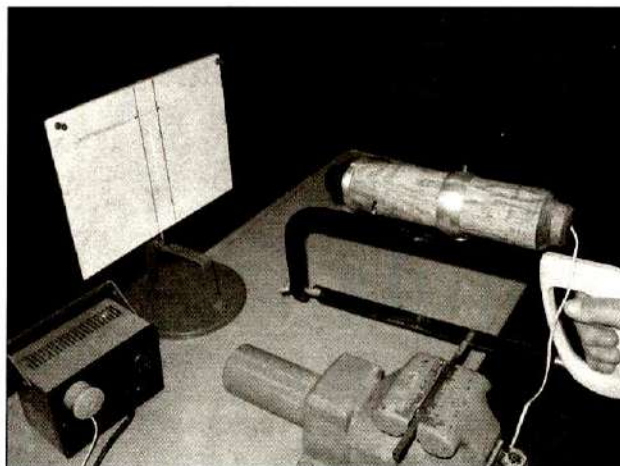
Приспособление 5 для формирования умения работать ножовкой
